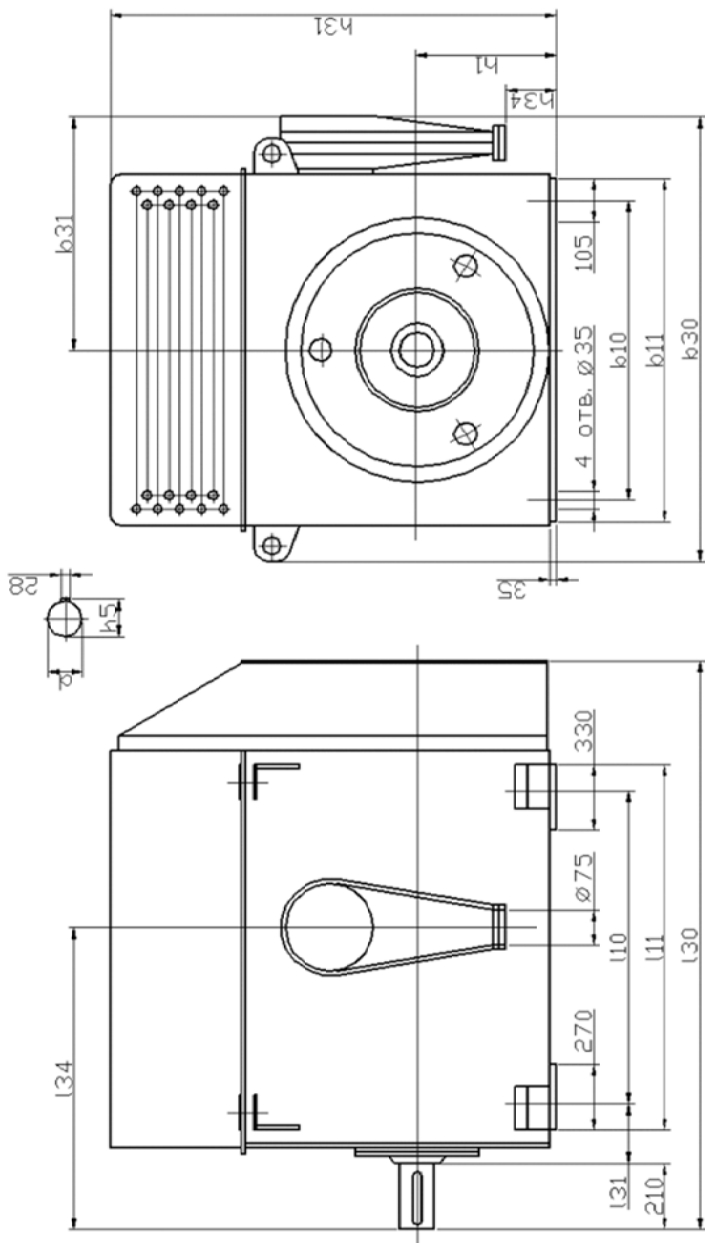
Габаритные и установочные размеры двигателей серии ДКВ
